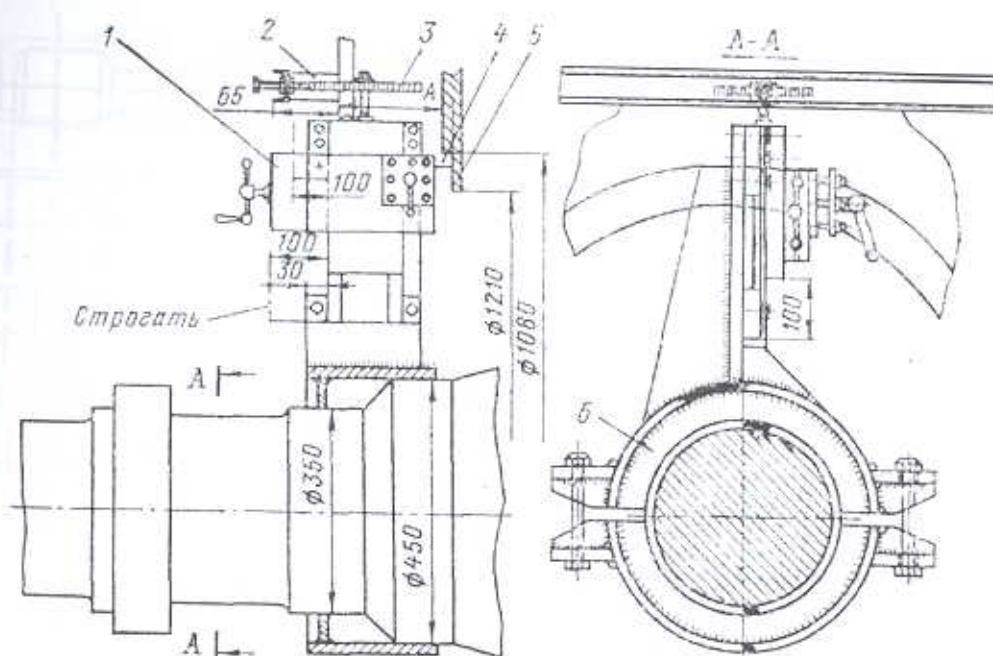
Приспособление для проточки привалочных поверхностей шита;
